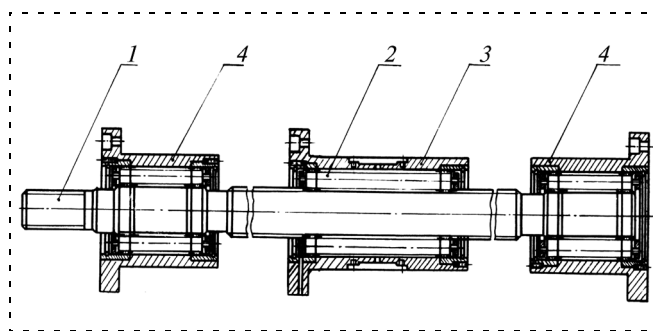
Планетарная передача с резьбовыми роликами типа SR с опорными гайками:
